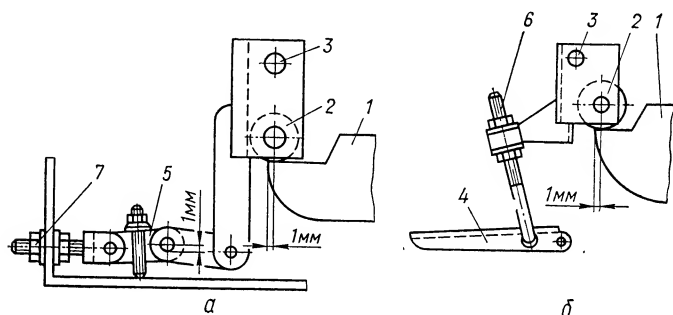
Узел для регулировки механизма включения привода ППМ-10:
